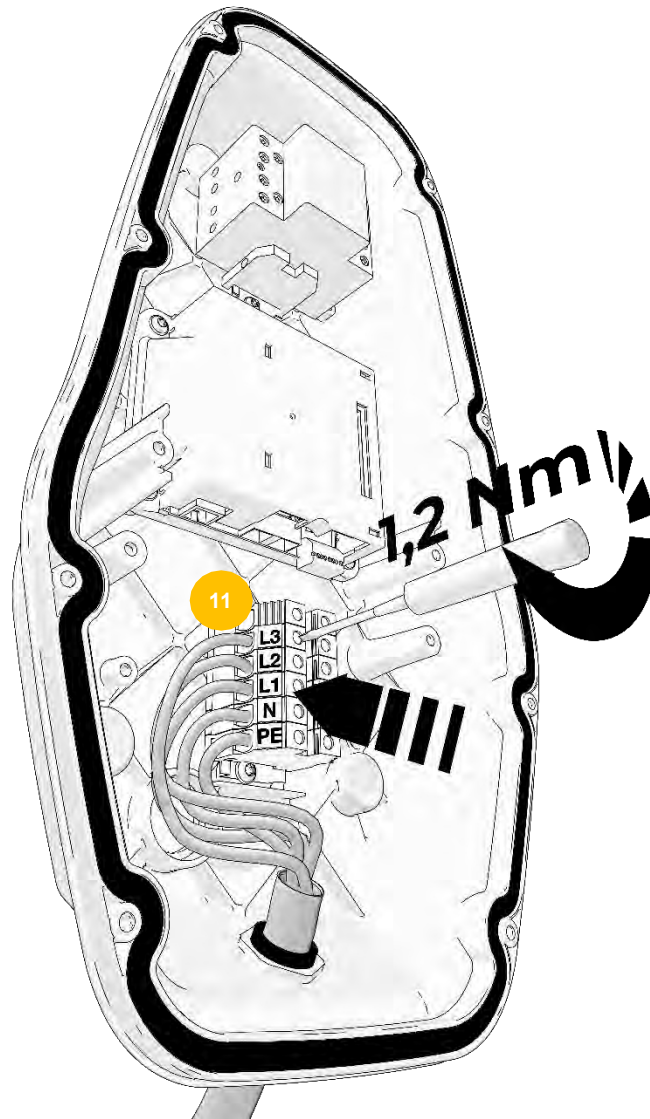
Collegamento del cavo di alimentazione alla morsettiera - Collegamento trifase
